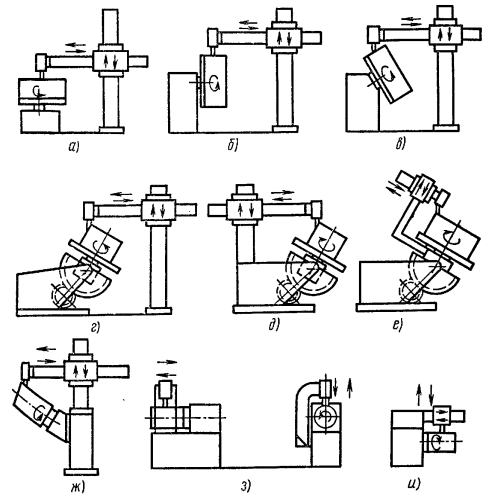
Типовые схемы компоновки установок и станков для электродуговой сварки круговых швов и наплавки поверхностей тел вращения изделий, закрепляемых консолями
